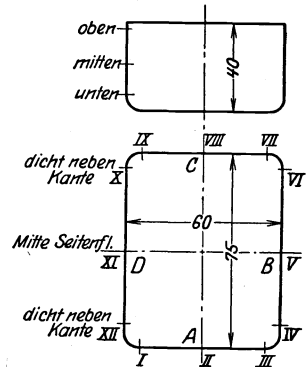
Änderung der Blechdicke beim Ziehen rechteckiger Hohlgefäße.
